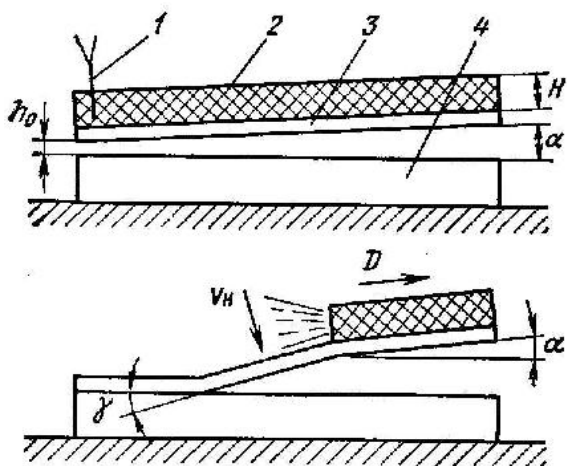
Принципиальная схема сварки взрывом
